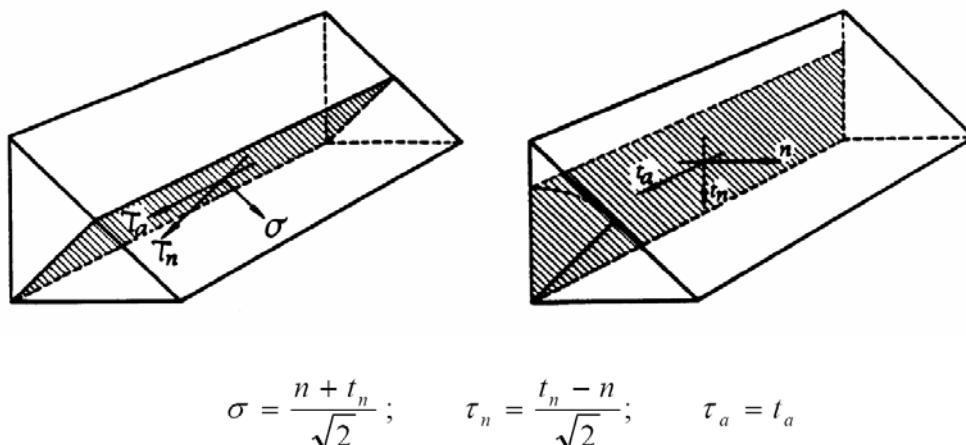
PLANO DE GARGANTA Y PLANO ABATIDO. RELACIÓN ENTRE LAS TENSIONES
